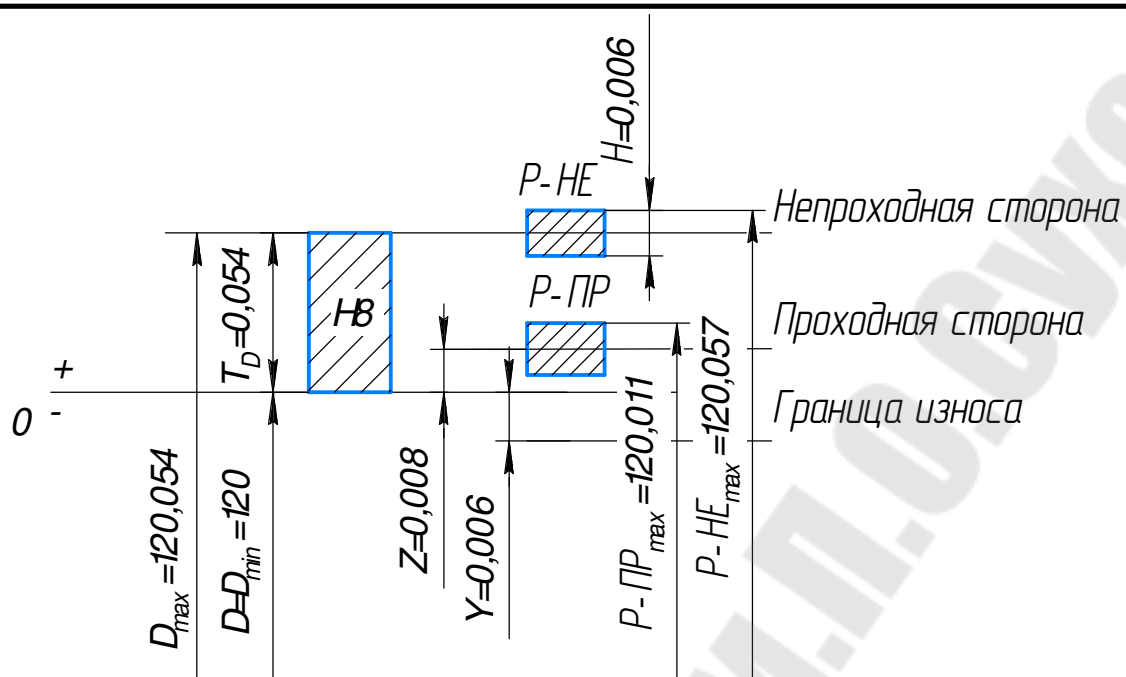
Схема расположения полей допусков рабочих калибров
